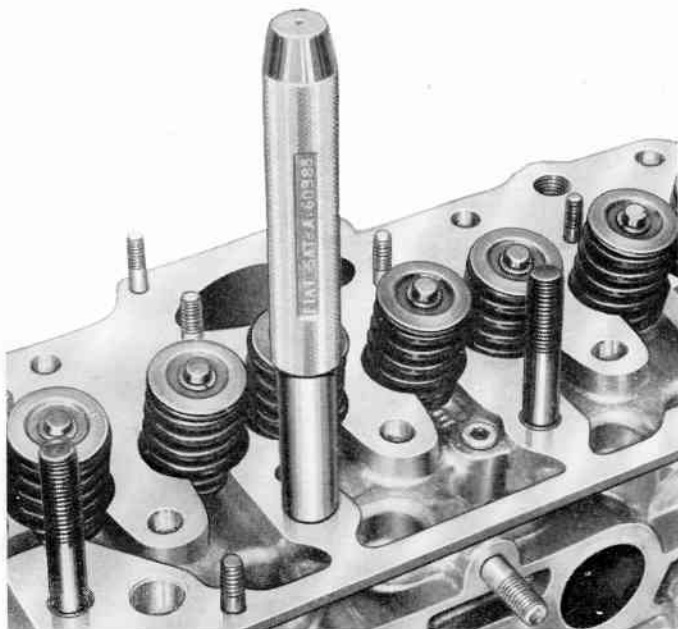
Verstemmen der Stiftschrauben zur Befestigung der Kipphebelböcke am Zylinderkopf mit dem Werkzeug A. 60288.
